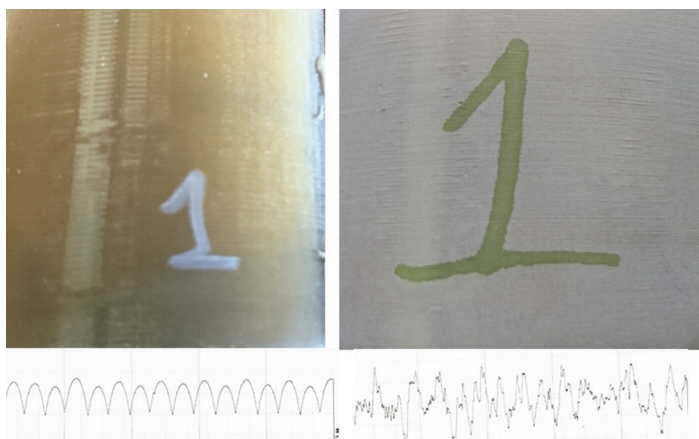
Внешний вид и профиль шероховатости образца до и после обработки грубой фракцией
